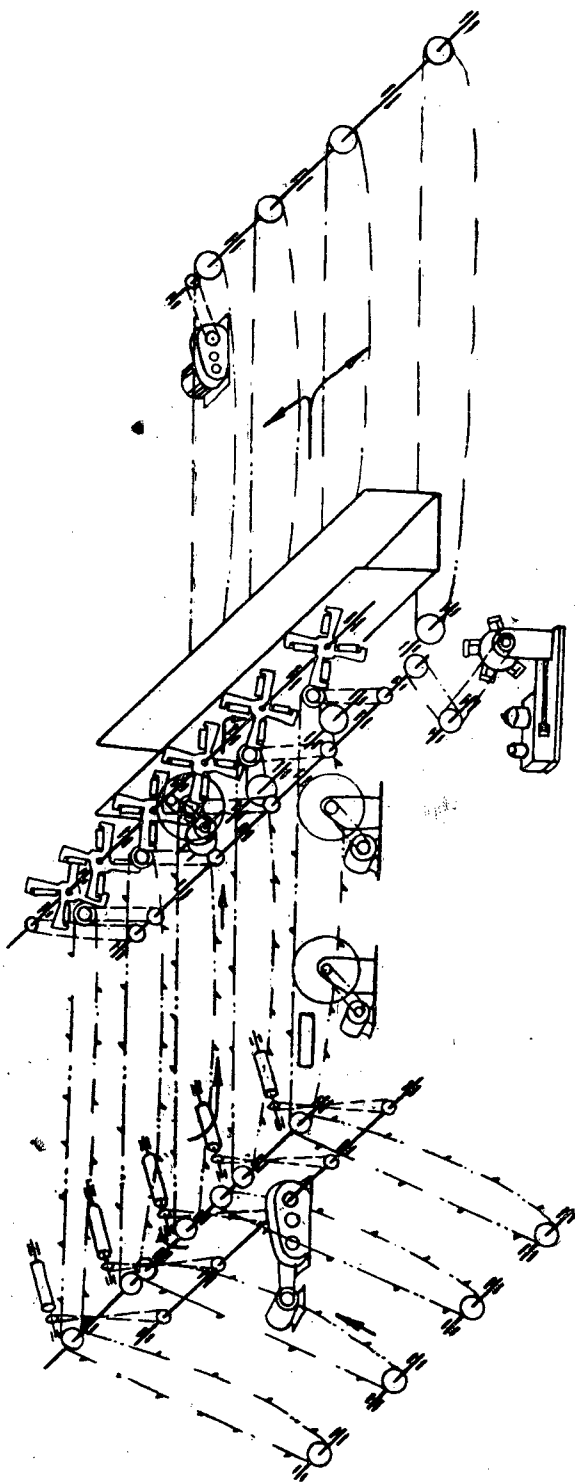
Кинематическая схема торцовочно-браковочной установки БТУ-1.
